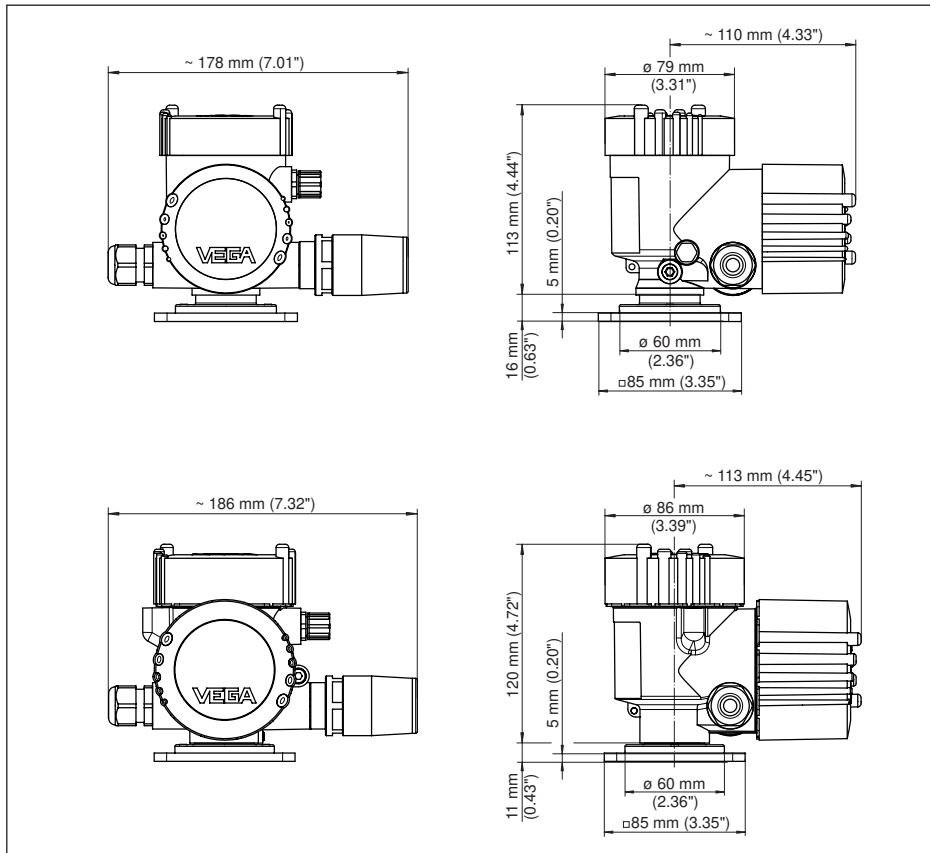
Размеры PLICSMOBILE T81 с пластиковым корпусом и корпусом из нержавеющей стали/ алюминия
